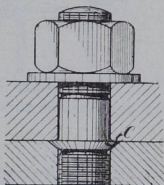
Stiftschrauben mit Bund zum Verstemmen.
